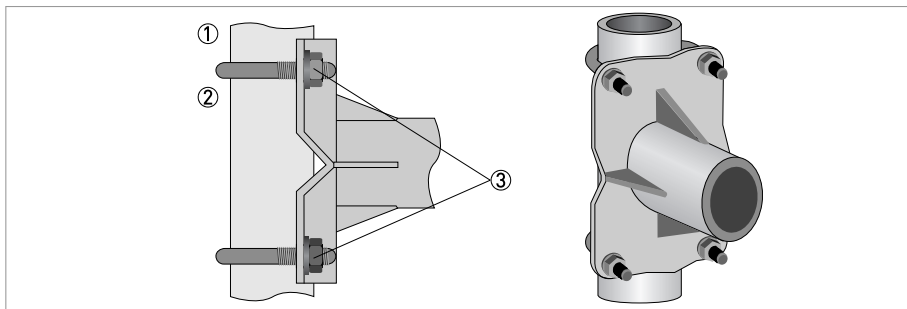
Крепление корпуса конвертера полевой версии
